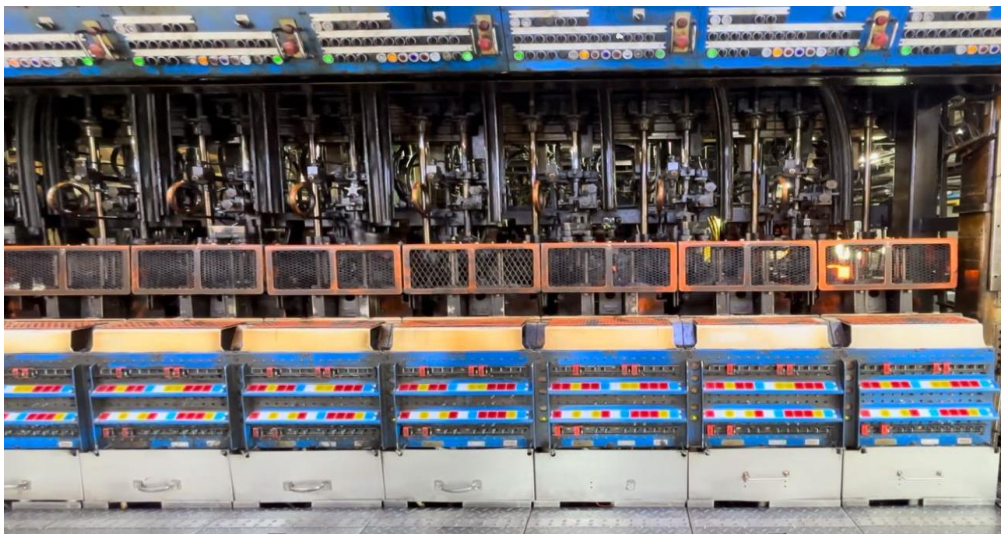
Máquinas formadoras de gota de vidrio. Fuente: Empresa manufacturera de vidrio, 2024.
